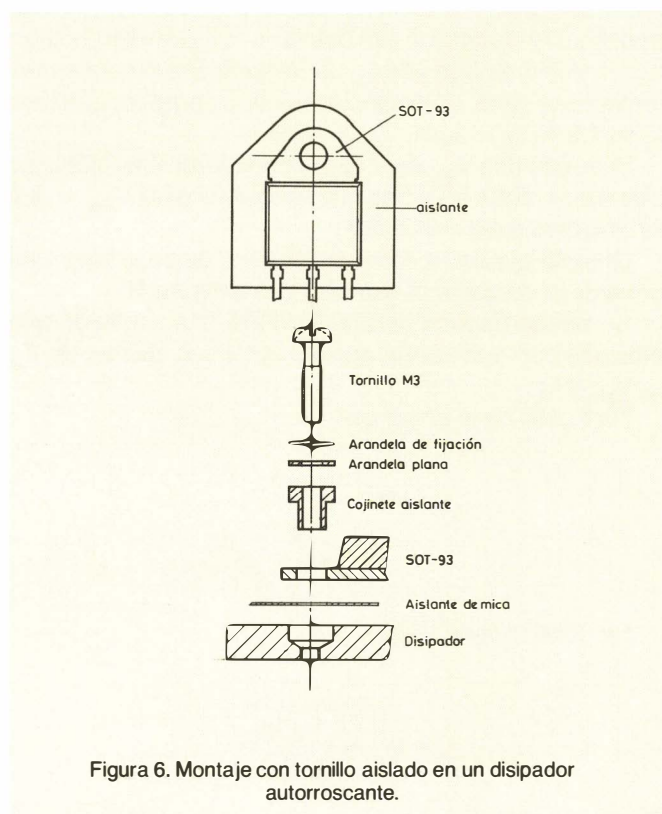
Montaje con tornillo aislado en un disipador autorroscante.
